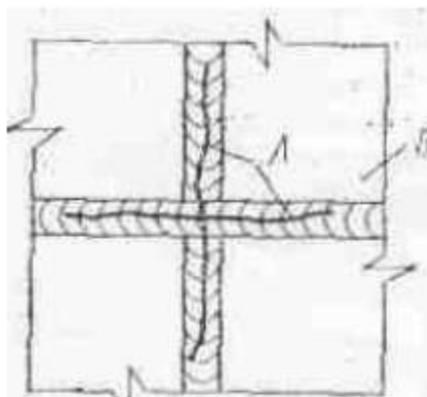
Продольные трещины А или одна трещина в пересечении сварных соединений стенки Б резервуара
